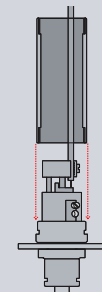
zu Schritt 6: Verbinder mit Gehäuse
